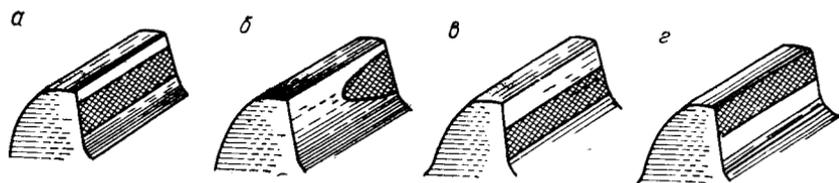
Проверка на краску зацепления зубчатых колес:
